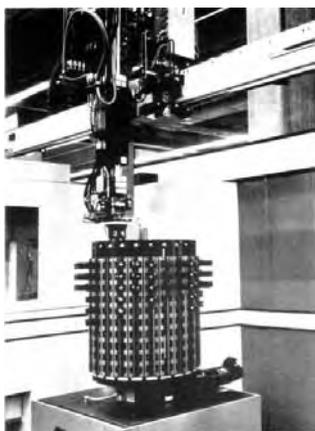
Система смены инструментов токарного многоцелевого станка Heunumat 35 фирмы Heuylingenstaedt Werkzeugmaschinen GmbH: 1 — основной магазин; 2 — линейный робот-манипулятор; 3 — промежуточный магазин; 4 — инструментальная головка
